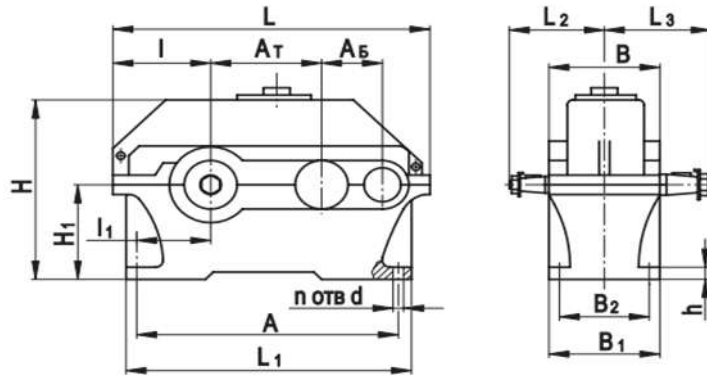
Редуктор циліндричний горизонтальний
